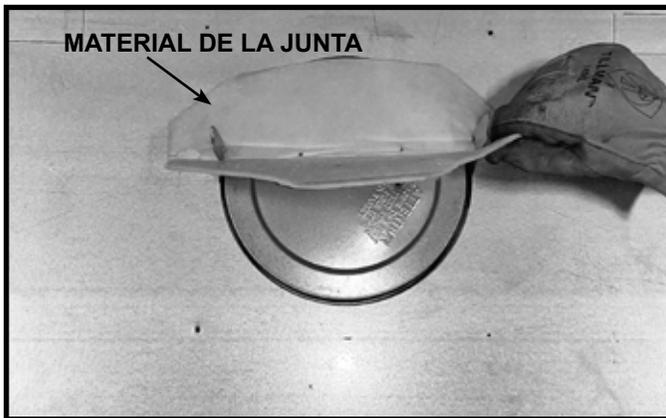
Retiro del material blanco de la junta que cubre la tapa de sellado
